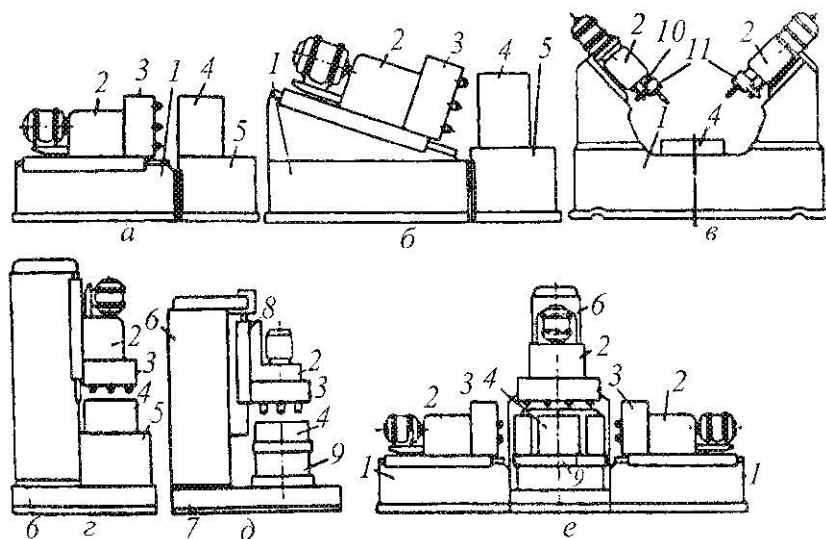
Схеми компоновок агрегатних свердлильних верстатів
